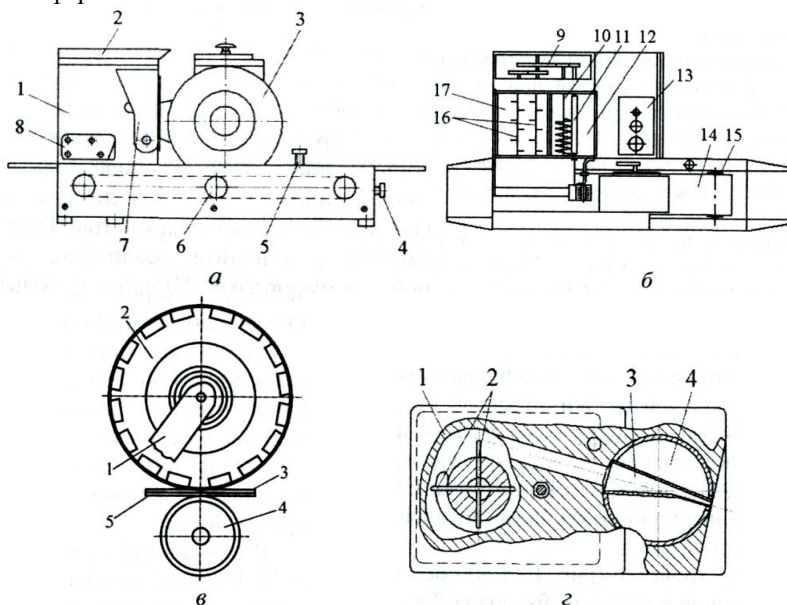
Агрегат для приготовления пельменей и вареников Л5-ФАП: а - общий вид автомата; б - вид сверху: 1 — станина; 2 — крышка; 3 — штампующий барабан; 4 - винт натяжной; 5 - регулировочный винт; б - опорный ролик; 7 - бункер для муки; 8 - формующая головка; 9 — привод; 10 - тестовый шнек; 11- тестовый барабан; 12 — бункер для теста; 13 - пульт управления; 14 - лента конвейера; 15 - натяжной ролик; 16 - фаршевые шнеки; 17 - бункер для фарша; в - штампующее устройство: 1 - рычаг; 2 - штампующий барабан; 3 - лоток; 4 - опорный ролик; 5 - лента транспортера; г - формующая головка: 1 - корпус; 2 - лопасть; 3 - канал подачи фарша; 4 - канал подачи теста.
